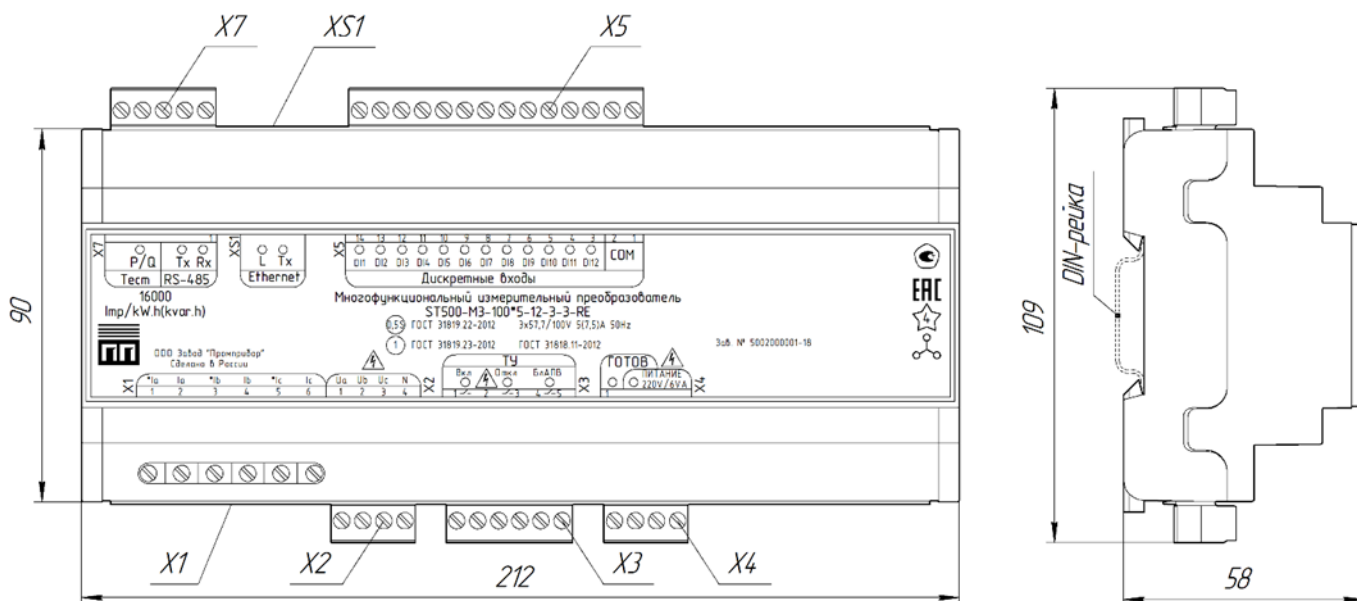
Внешний вид и габаритные размеры МИП ST500-M3-XXX*X-12-3-3-RE и ST500-M3.02-XXX*X-12-3-3-RE
